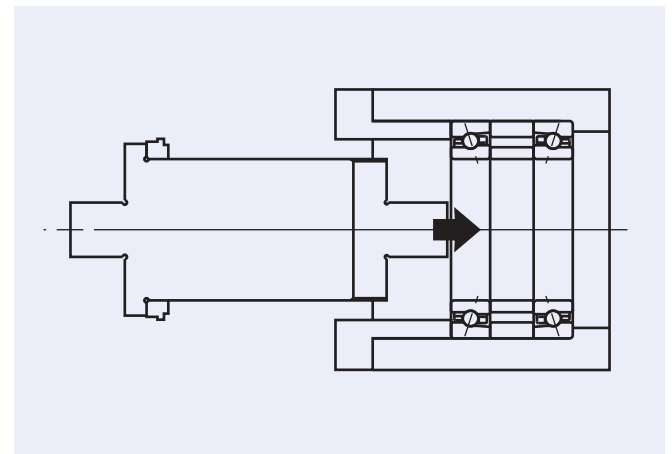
Montaggio con Disposizione Faccia a Faccia
